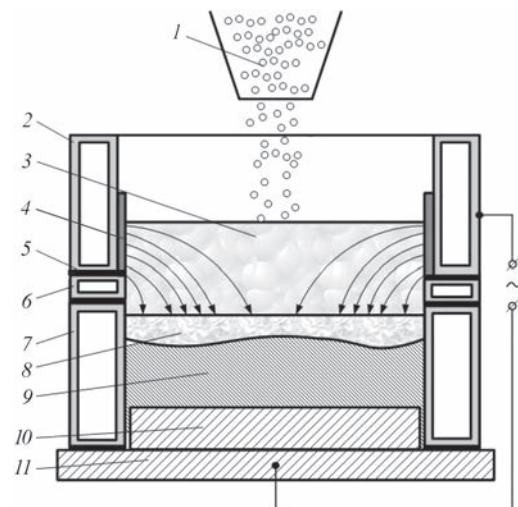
Схема ЕШН дискретною присадкою в СПК: 1 – дискретна присадка; 2, 6, 7 – струмопровідна, проміжна і формуюча секції кристалізатора відповідно; 3 – шлакова ванна; 4 – захисне футерування; 5 – ізоляційна прокладка; 8 – металева ванна; 9 – наплавлений метал; 10 – виріб; 11 – піддон. Стрілки показують розподіл струму в шлаковій ванні
